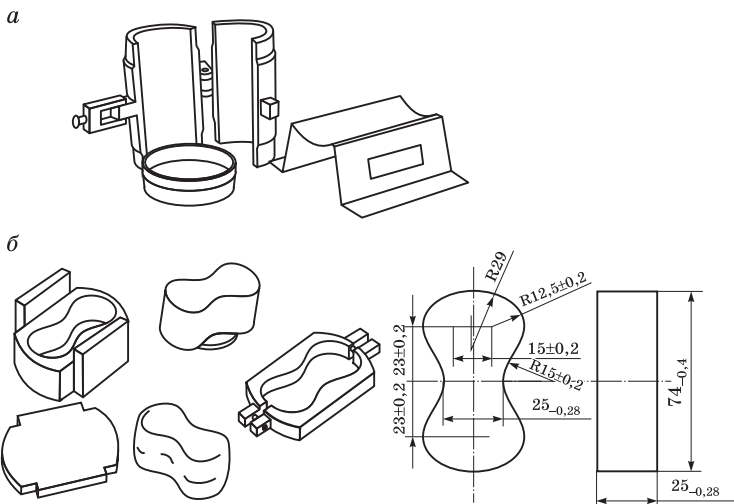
Стержневые ящики для изготовления стандартных образцов:
